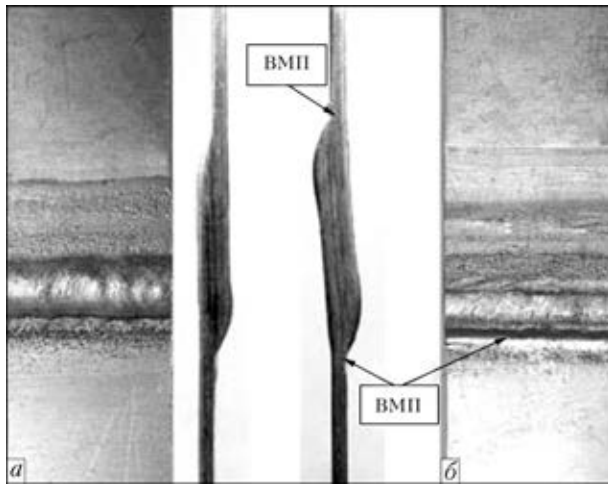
Образцы нахлесточного сварного соединения в исходном после сварки состоянии (а) и после ВМП зон сплавления (б)
